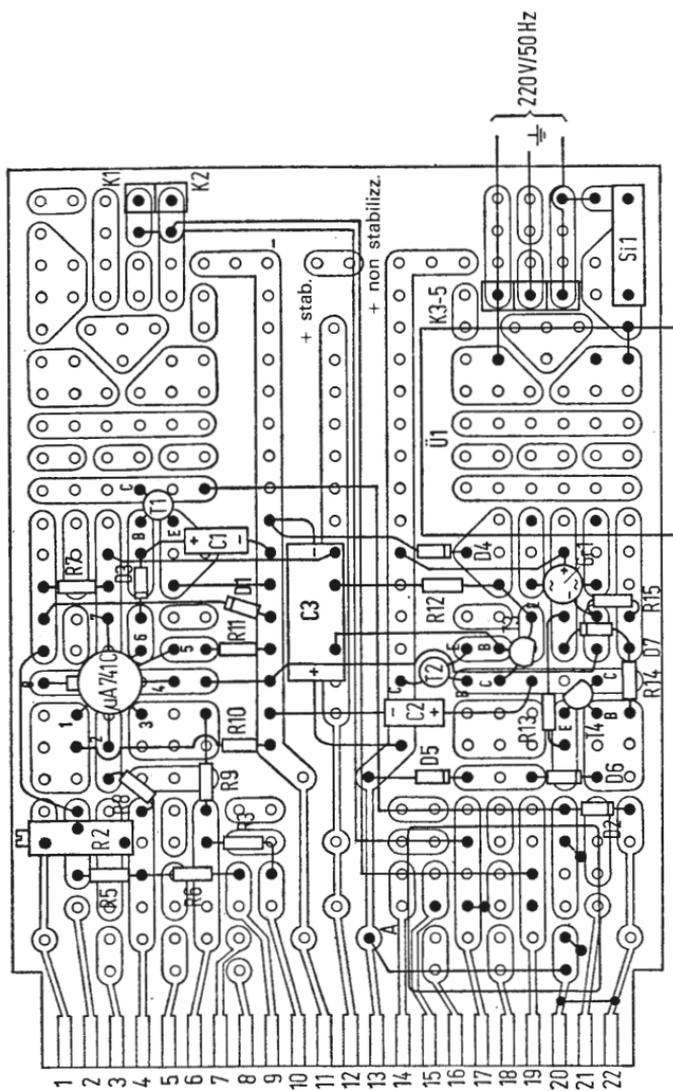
Disposizione dei componenti del circuito di fig. 21 vista dal lato isolante del circuito stampato
